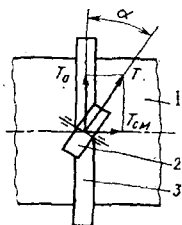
Схема перекоса ролика: 1 – барабан; 2 – опорный ролик; 3 – бандаж; T – окружная сила трения пары ролик-бандаж; T_{cm} – сила, смещающая барабан вдоль оси.
